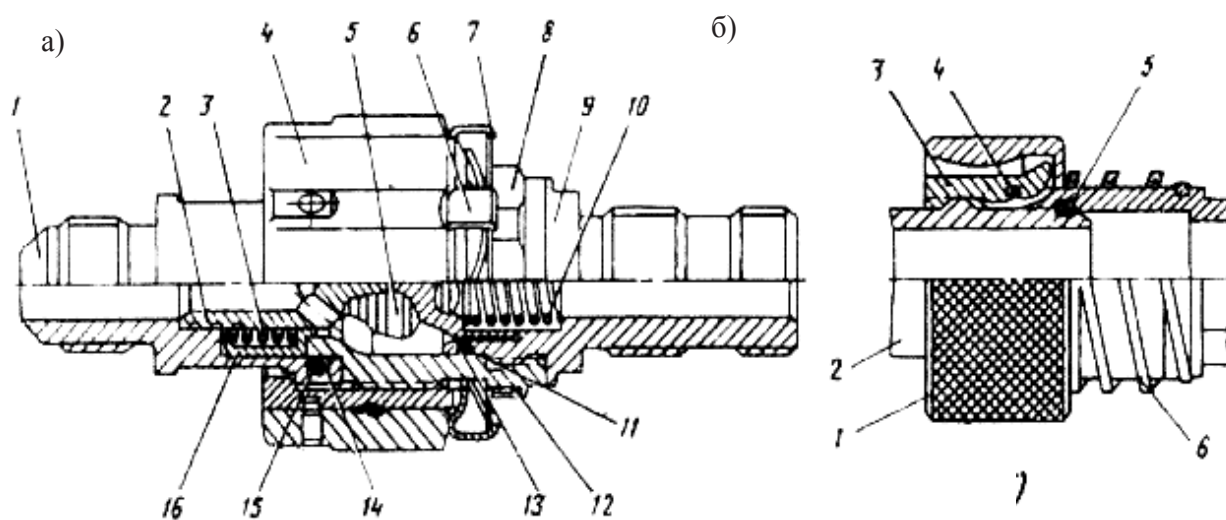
Схемы быстроразъемных неподвижных беспрокладочных соединений трубопроводов: а – разъемный клапан: 1 – штуцер; 2 – клапан; 3, 10 – пружины; 4 – гайка в сборе (гайка, обойма, штифт); 5 – клапан; 6 – пружина; 7 – контрольная шайба; 8 – корпус; 9 – штуцер; 11, 15 – уплотнительные кольца; 12 – обойма; 13, 14 – защитные шайбы; 16 – втулка; б – цангового типа: 1 – обойма; 2 – наконечник; 3 – кулачок; 4 – кольцо; 5 – уплотнительное кольцо; 6 – пружина
